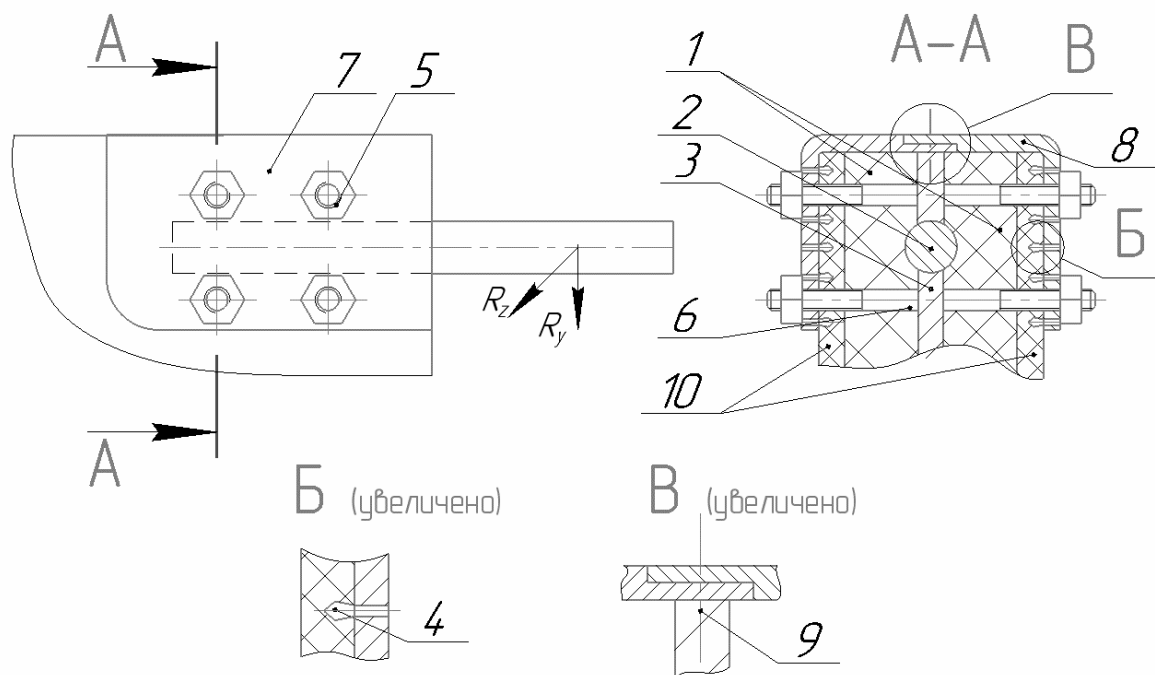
Соединение борта транспортного средства с металлическим элементом опоры А: 1 – слой из композитных пластинок; 2- палец; 3 – металлический лист, соединенный с пальцем; 4 – копьеобразный крепежный элемент; 5 – гайка; 6 – шпилька; 7, 8 – металлическая пластина; 9 – винты; 10 – препрег обшивки борта
